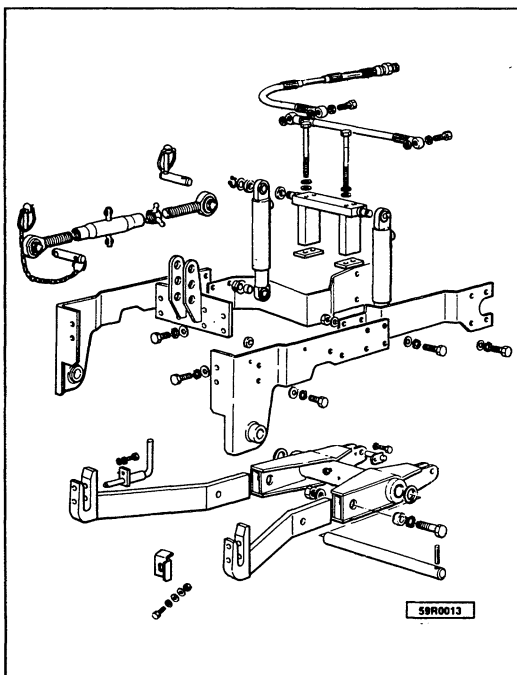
Piezas componentes del grupo de elevación delantero.
